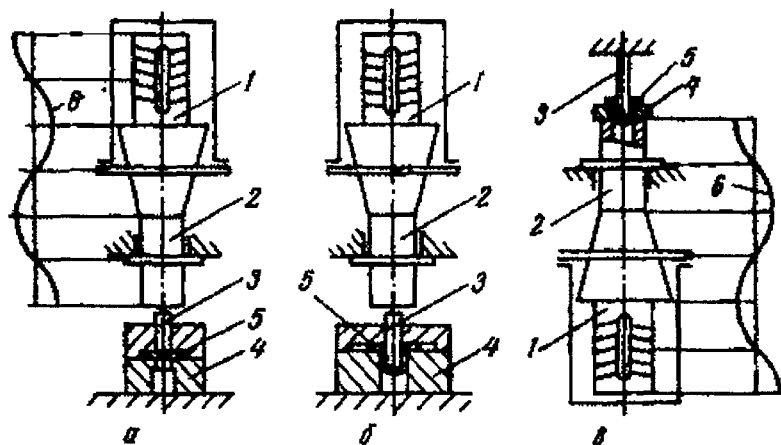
Колебательные системы с незакрепленным инструментом для вырубке-пробивки (а) и вытяжки (б, в):
